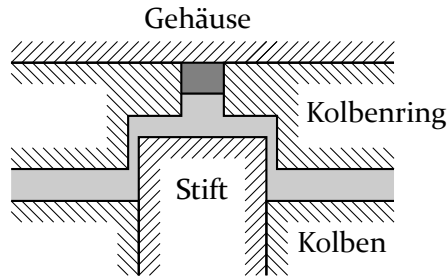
Detailskizze des Stoßes eines eingebauten Kolbenrings mit Verdrehsicherung.
